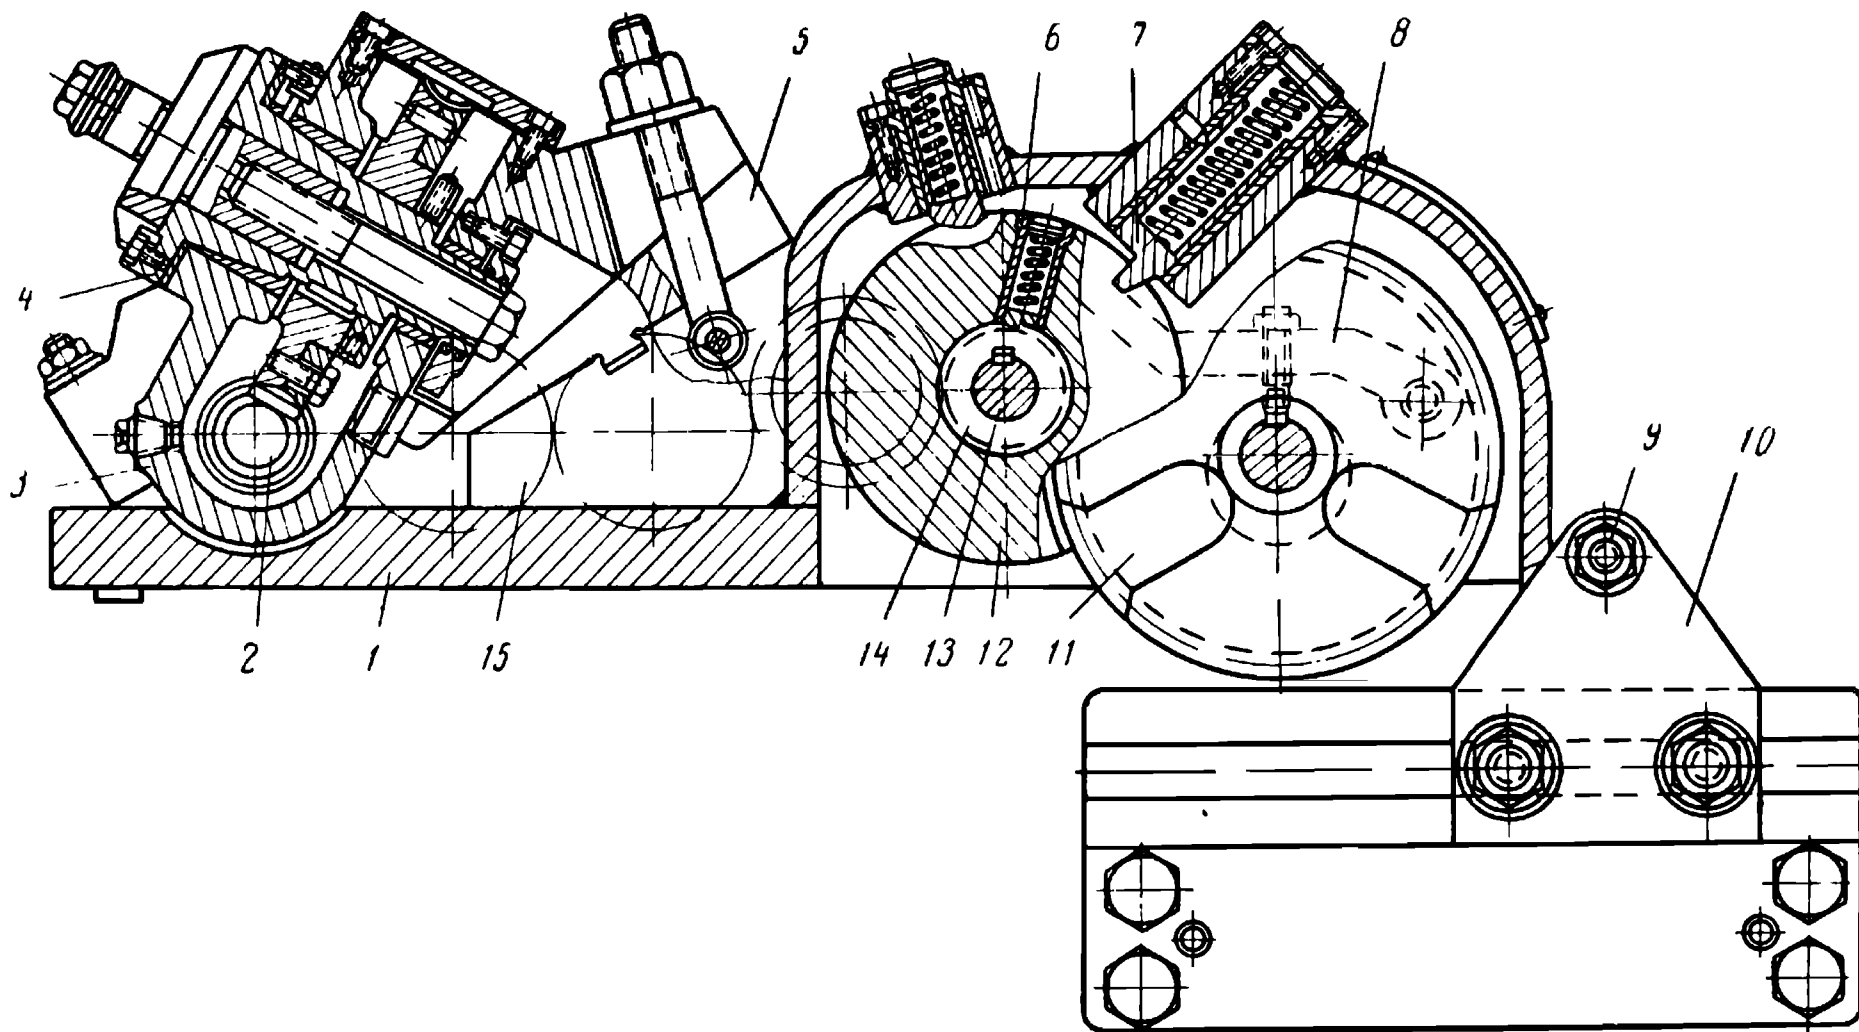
Приспособление для полуавтоматического нарезания конических колес на горизонтально-фрезерном станке
